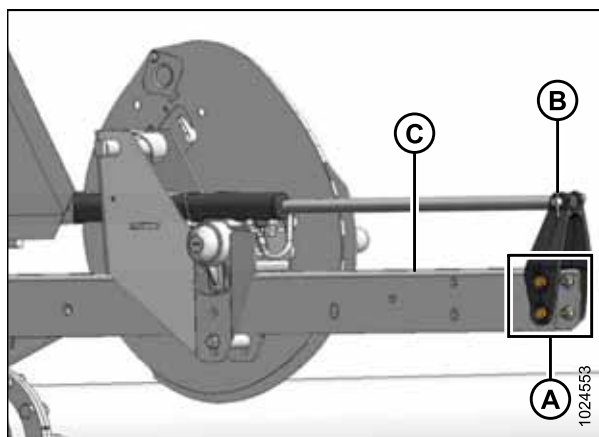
Cilindro do braço direito do molinete em posição de avanço
